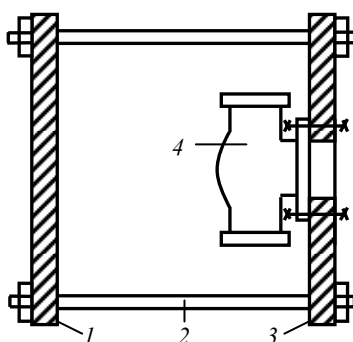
Устройство для проточки седла клапана вентиля:
